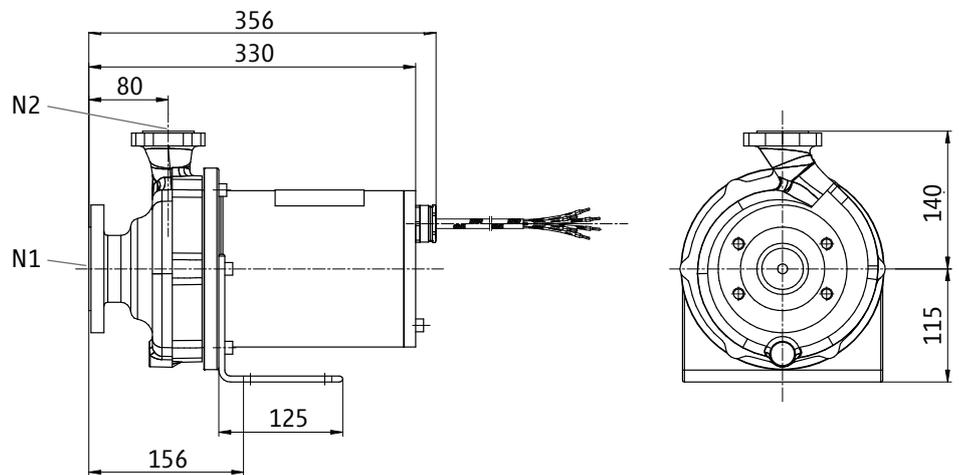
Maßzeichnung LC32-125 mit AGX1.8 Motor, HERMETIC
